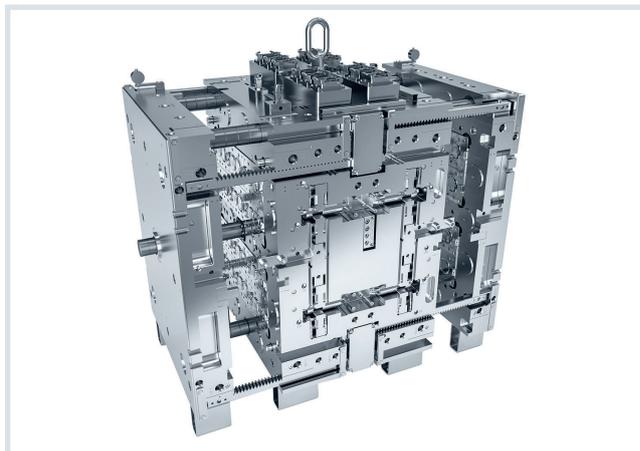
Modular aufgebautes, kompaktes 12+12-fach Etagenwerkzeug mit Nadelverschluss-Vollheißkanalsystem
